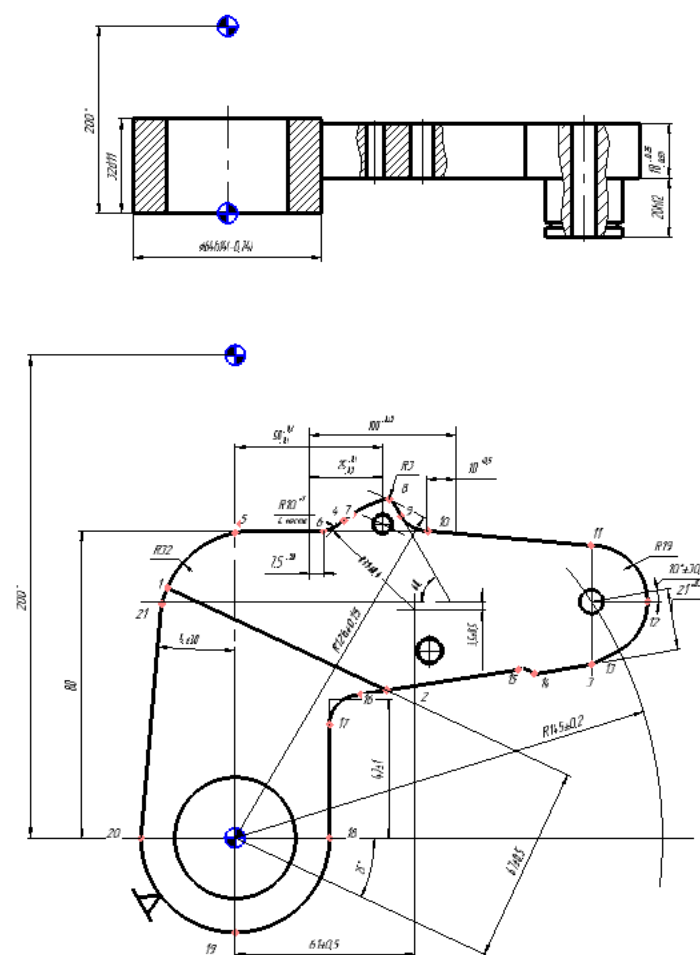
Схема базирования заготовки на операции 015 установ Б
